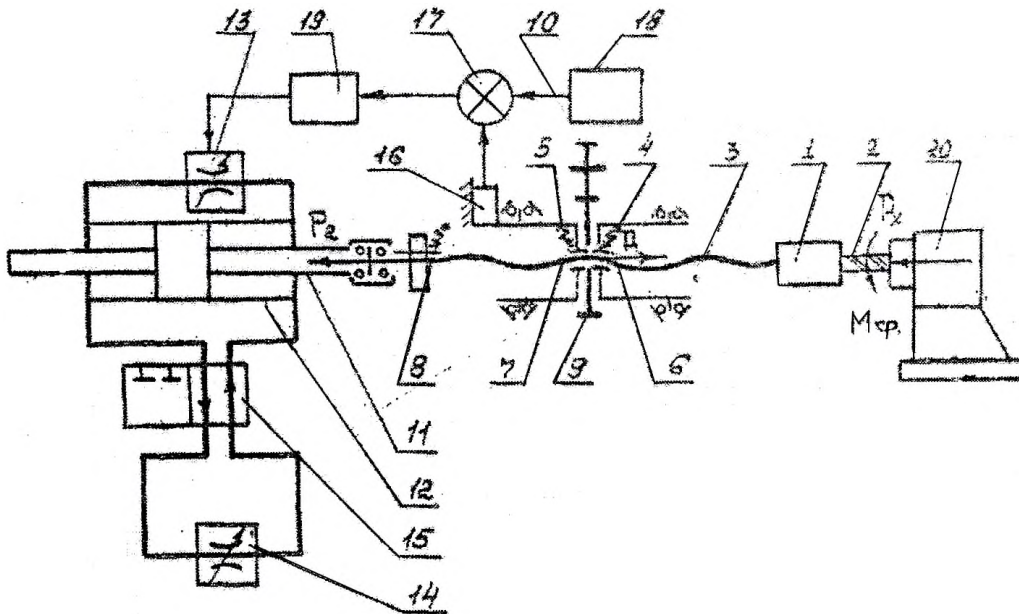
Шпиндельний вузол металорізального верстата [17]
